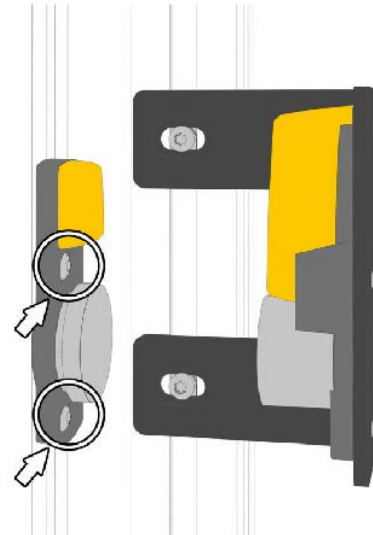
Ankerplatte am Profil der Schiebetüre anbringen, zur Prozesszuhaltung ausrichten und zur Prozesszuhaltung ausrichten. Schrauben M6 x 16 mm Torx festziehen.
